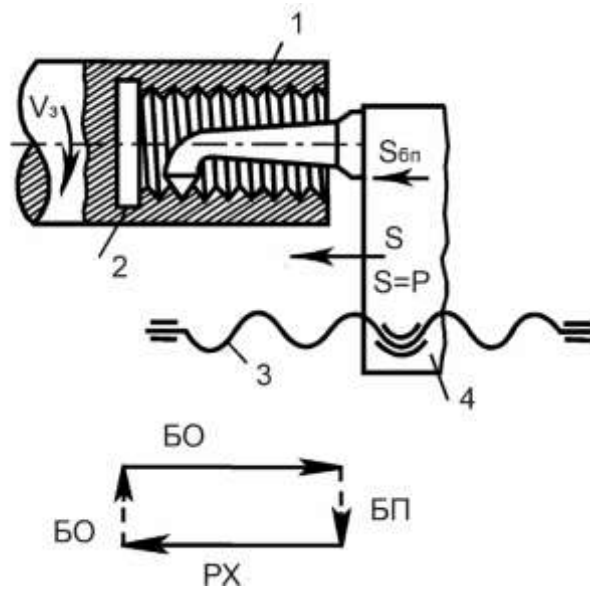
Схема обробки та циклограма роботи при нарізуванні внутрішнього різьблення: 1 – заготовка; 2 – різьбова поверхня; 3 – ходовий гвинт; 4 – супорт із встановленим різцем.
